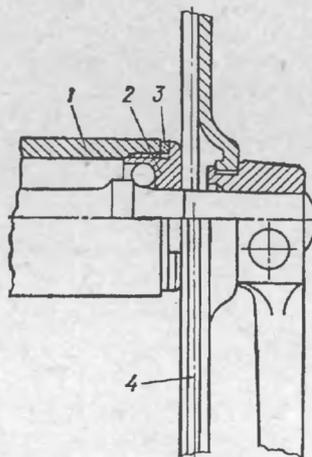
Постановка регулировочного кольца под чашечку каретки велосипеда (сечение Б—Б на рис. 58):
